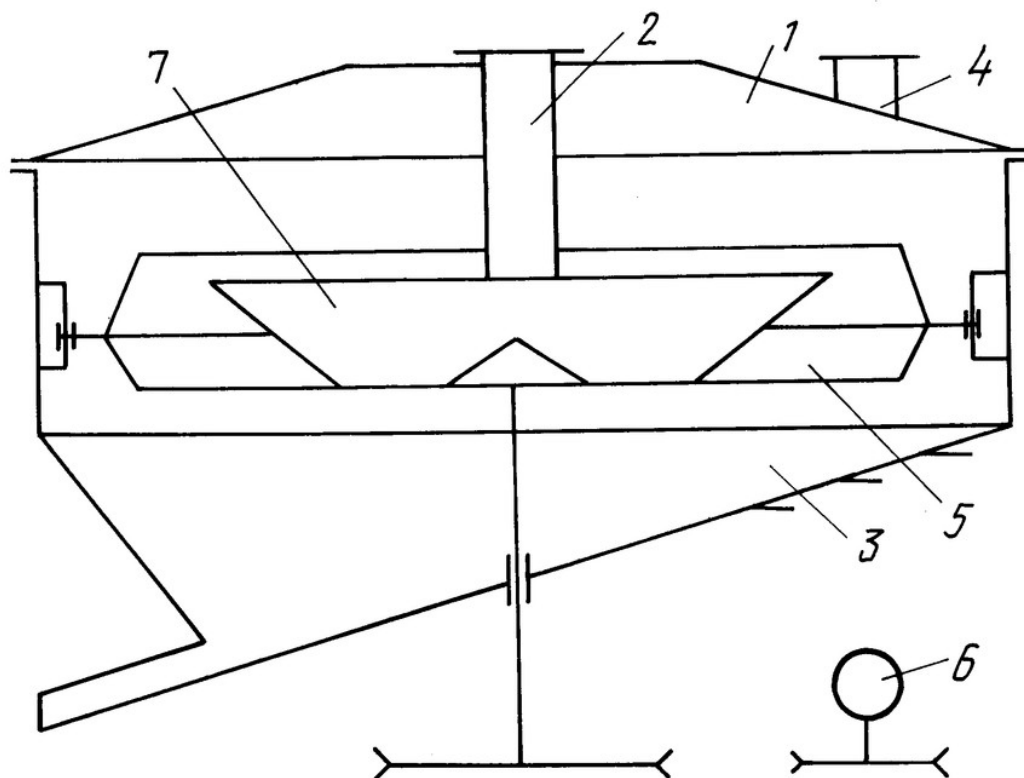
Шелушитель зерна по патенту №2143321
